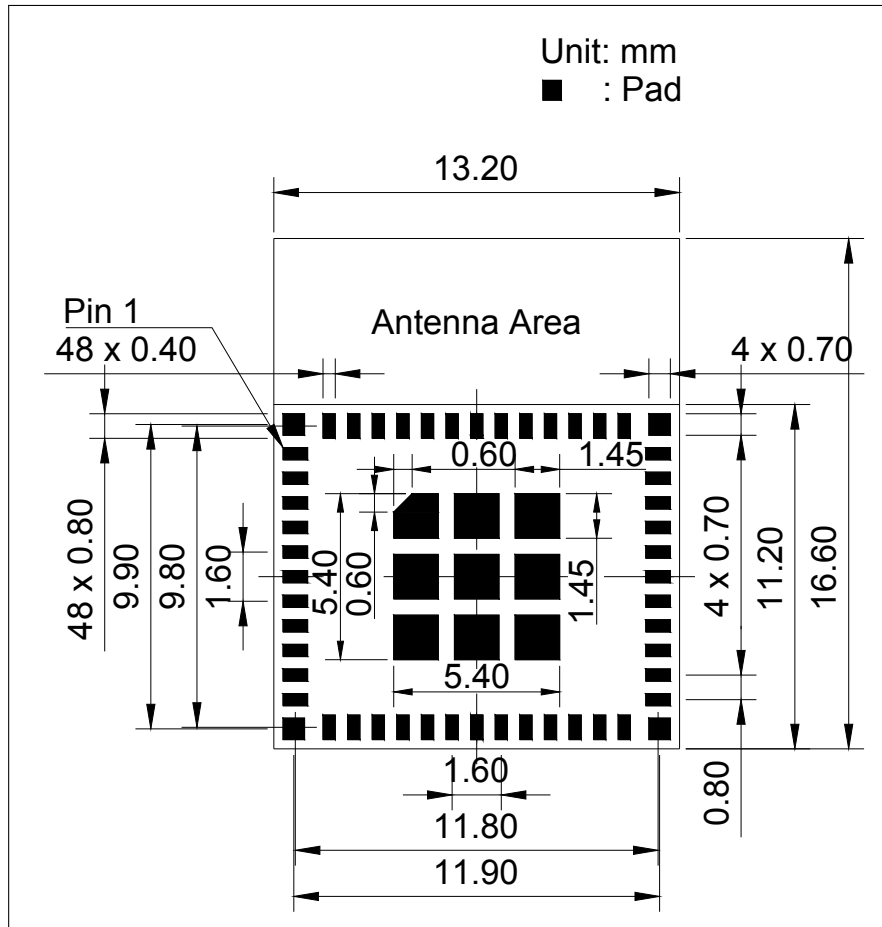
ESP32-C6-MINI-1 推荐 PCB 封装图形
